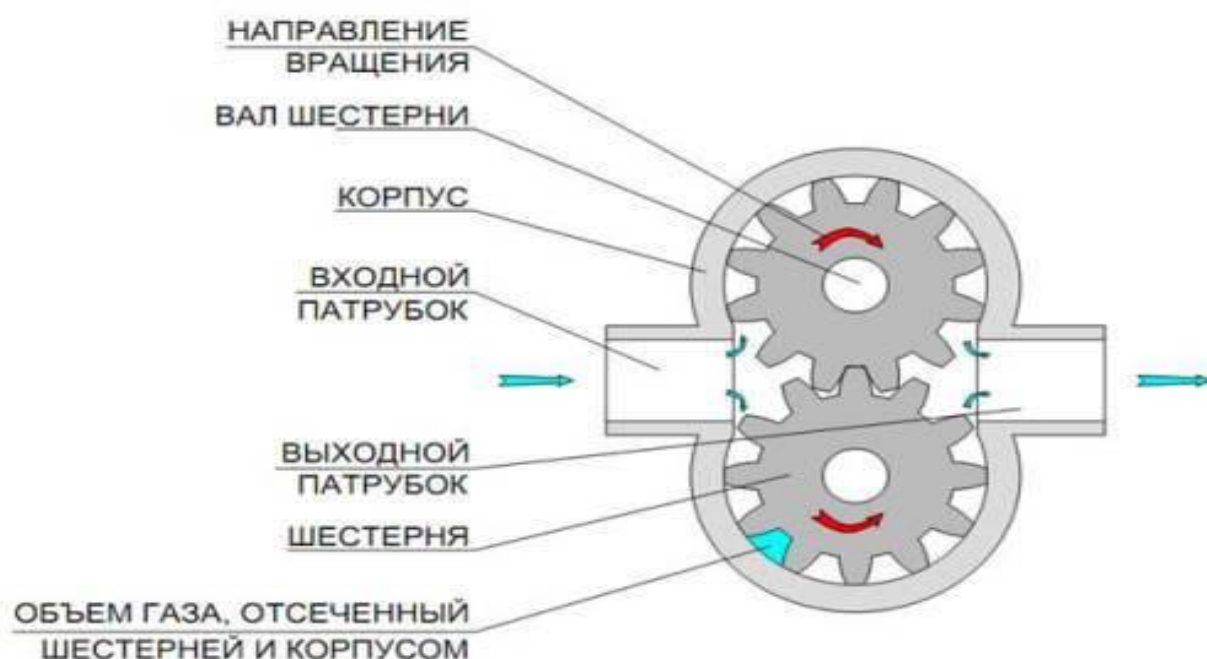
Чертеж шестеренчатого компрессора.
